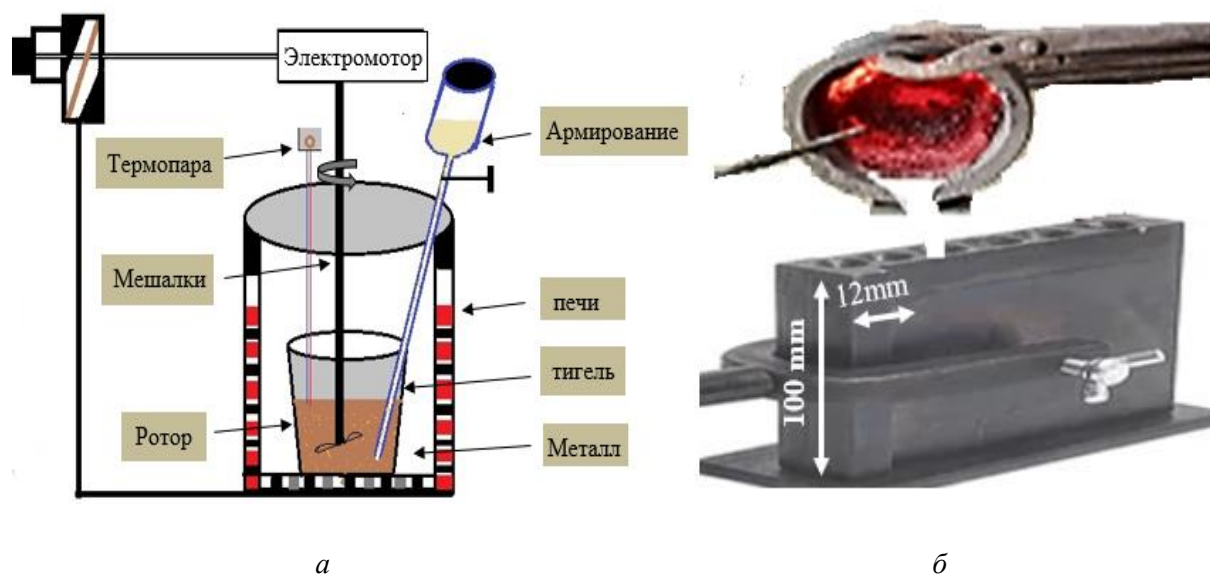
Схема печи для плавки с мешалкой (а) и литейная форма (б)
